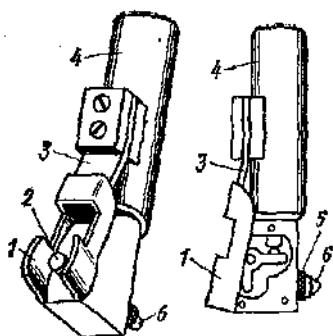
Корпус индикаторного нутромера для размеров от 18 до 50 мм:
